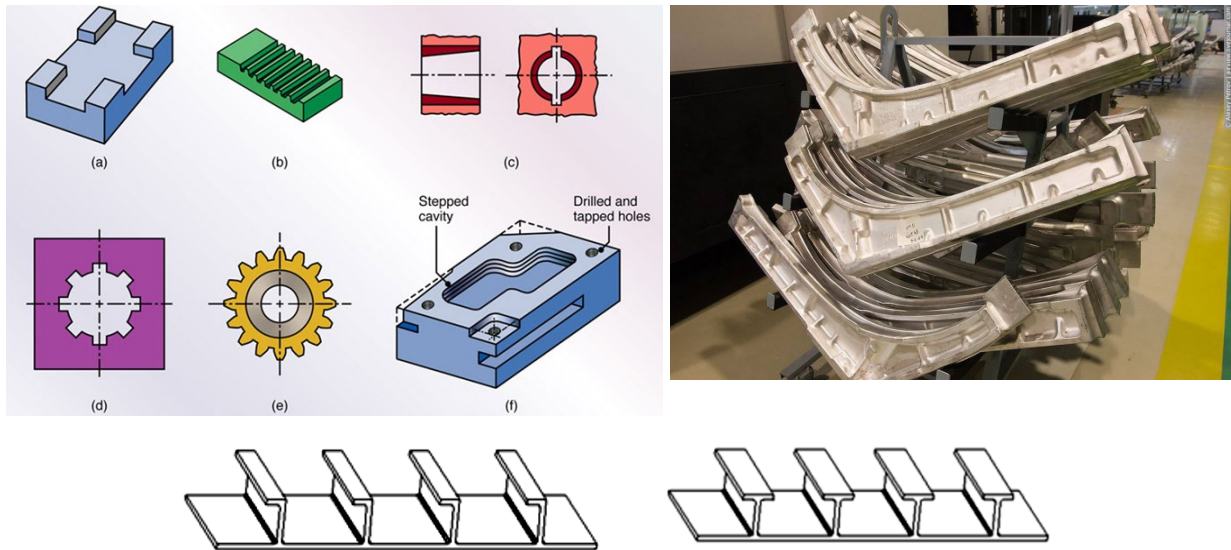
Типові фрезеровані деталі (а), фрезеровані шпангоути (б), фрезеровані монолітні панелі (в)
